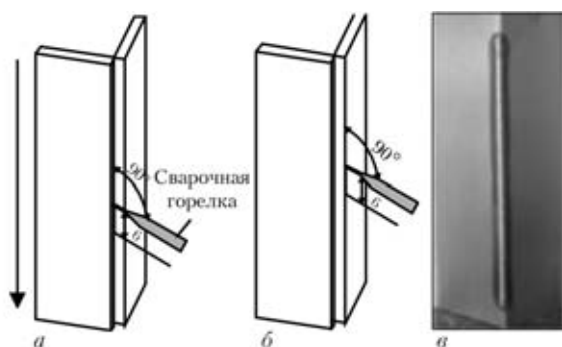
Выполнение обычной МАГ сваркой углового соединения при нулевом корневом зазоре (а, б) и внешний вид соединения (в): а — горелка направлена по линии соединения; б — то же по кромке одной из пластин
